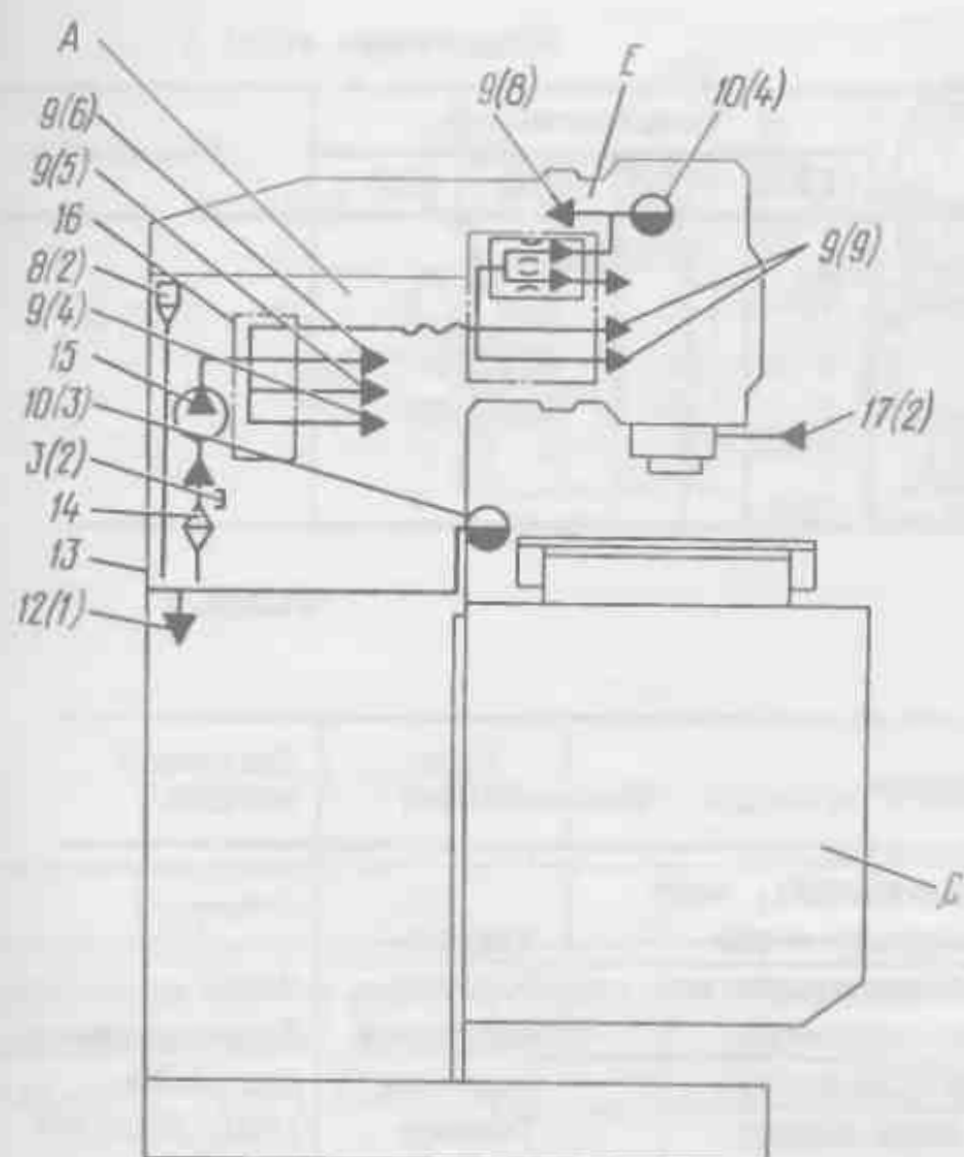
Принципиальная схема смазки станка 6Т10 (схему смазки привода подач С см. рис. 34)
